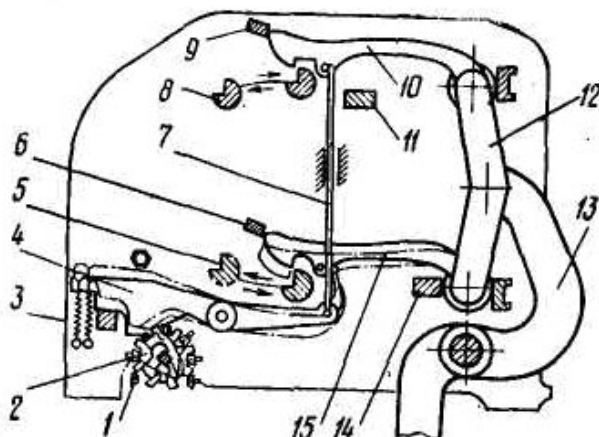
Зевобразовательная каретка СК-12 ткацкого станка АТПР:
